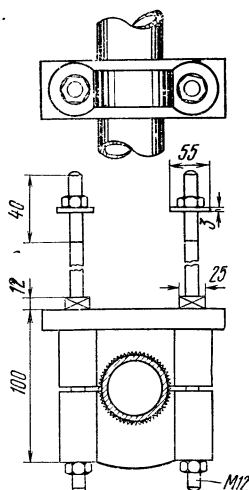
Чугунный хомут для крепления основания стойки к стропилам
